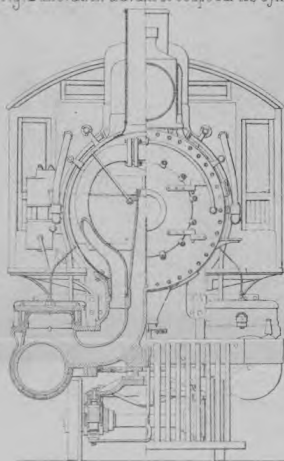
Elévation d'avant et Coupe sur les Cylindres.
